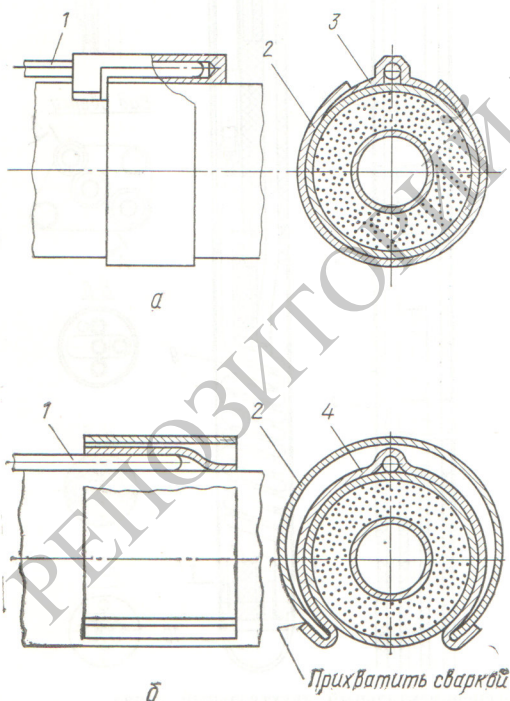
Способы крепления королька термопары с помощью колодки (а) и полоски фольги (б):
